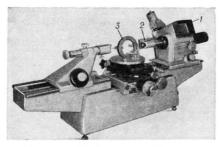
Оптический длиномер: 1 — проекционное устройство; 2 — измерительный стержень; 3 — измеряемая деталь.
